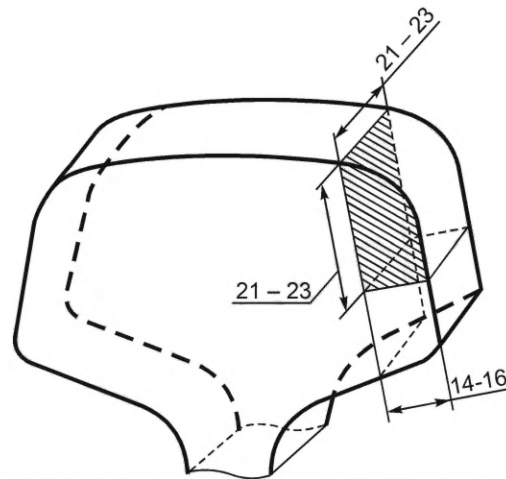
Схема расположения шлифа для контроля неметаллических включений
